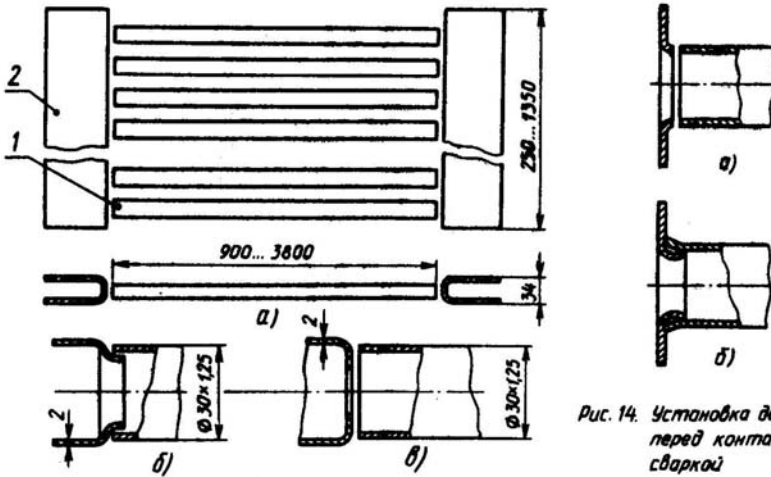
Заготовки труб и коллекторов (а), подготовленные для дуговой (б) и контактной (в) сварки
